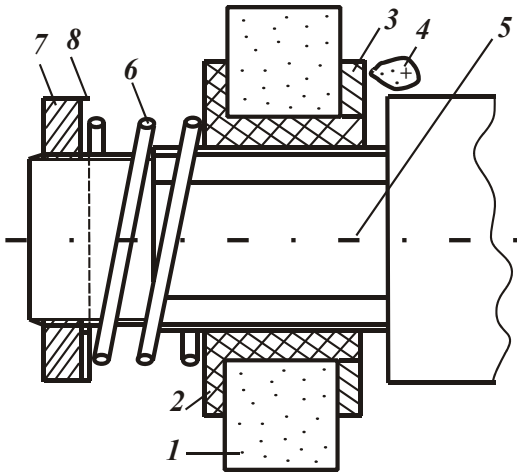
Устройство с осевым перемещением шлифовального круга: 1 – круг; 2 – шлицевая втулка; 3 – шайба или гайка; 4 – эксцентрик (показан повернутым на 90°); 5 – шлицевый вал с резьбой; 6 – пружина; 7 – гайка; 8 – шайба.
